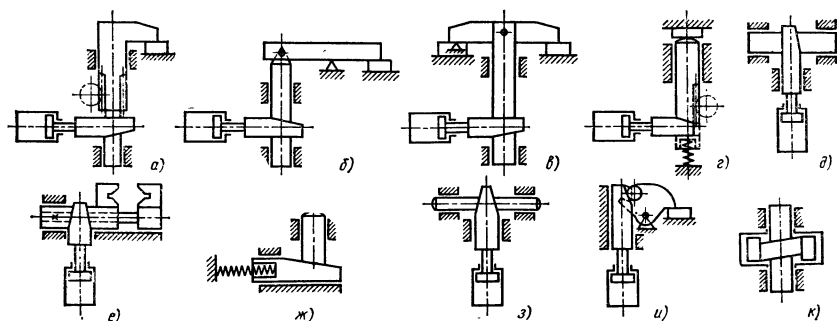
Схемы гидравлических и пневматических зажимных устройств приспособлений с усиливающей или самотормозящей передачей:
